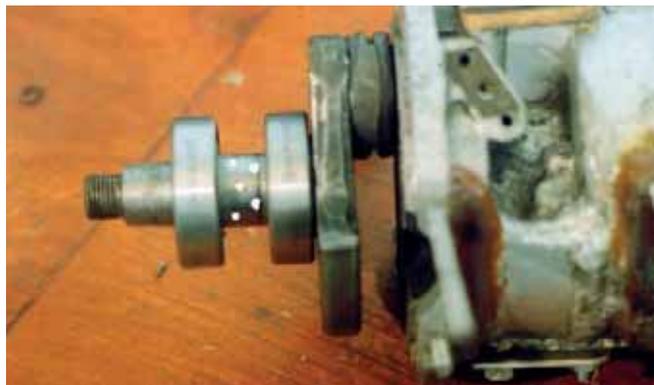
Методика прочной запрессовки шарикоподшипников открытого типа на верхнюю опору коленчатого вала. Белые точки — схема кернения посадочного места шарикоподшипника № 205 (верхнего)
